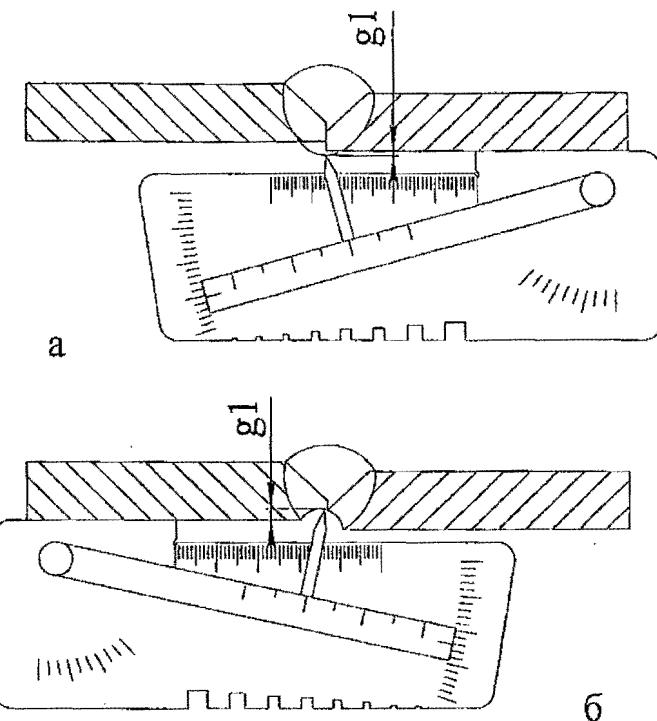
14. Измерение выпуклости (вогнутости) корня шва (g_1) стыкового сварного соединения при различном уровне поверхностей деталей, вызванном смещением при сборке соединения под сварку:
